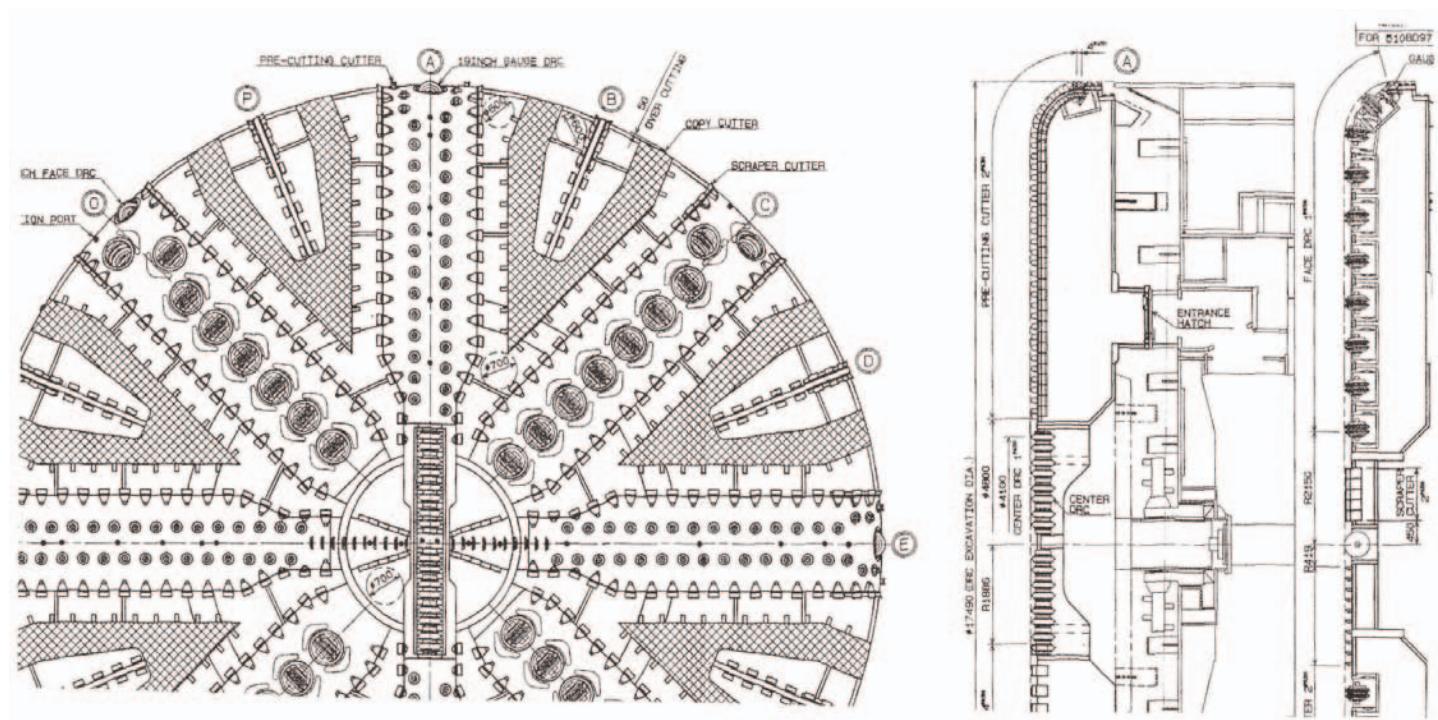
Esquema y detalle de un escudo EPB KAWASAKI/KAWASAKI EPB Shield. Cutterhead and cutter change schemes.
